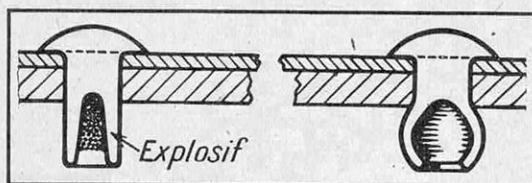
SCHÉMA DE LA POSE D'UN RIVET PAR EXPLOSION (PROCÉDÉ HEINKEL)
